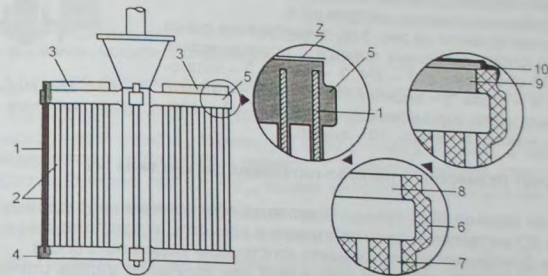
Схема модельного блока для изготовления литых сварочных электродов
